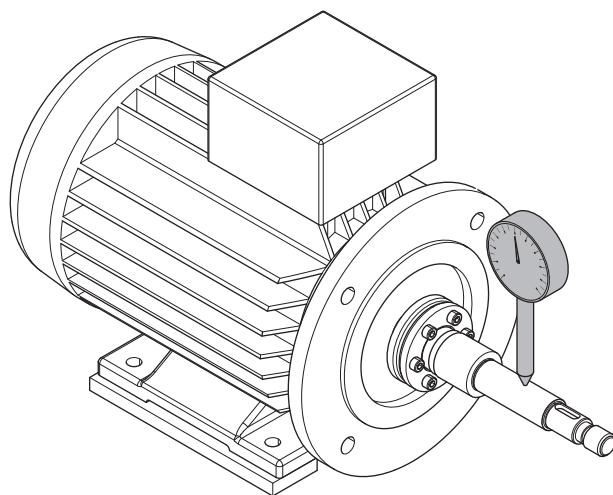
Tolerancia de excentricidad del eje de bomba
